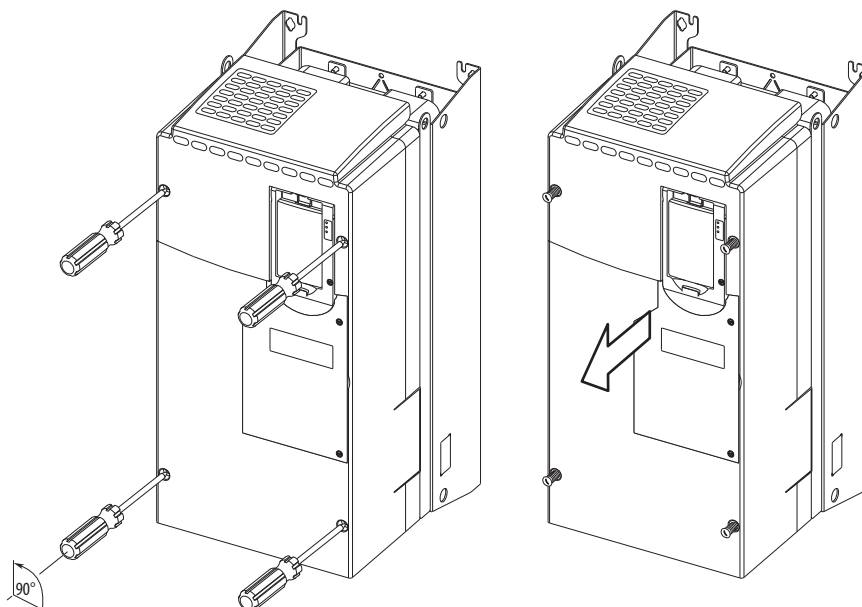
Код корпуса G (IP54, NEMA/UL Type 12), типоразмеры 2–5
